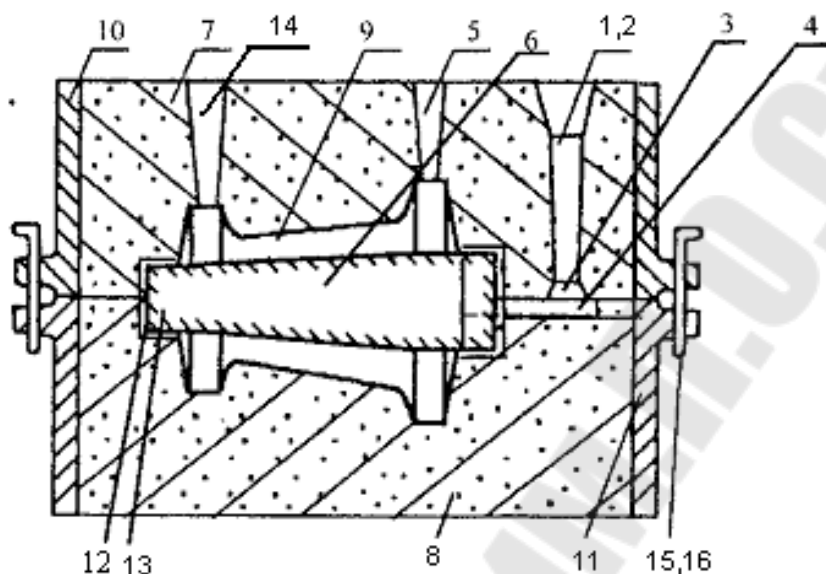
Литейная форма в сборе: 1 - воронка; 2 - стояк; 3 - шлаковик; 4 - питатель; 5 - прибыль; 6 - стержень; 7 - верхняя полуформа; 8 - нижняя полуформа; 9 - полость под отливку; 10 - верхняя опока; 11 - нижняя опока; 12 - замок стержневой зажим; 13 - стержневой зажим; 14 - вентиляционные каналы; 15 - центрирующая система; 16 - скобы
